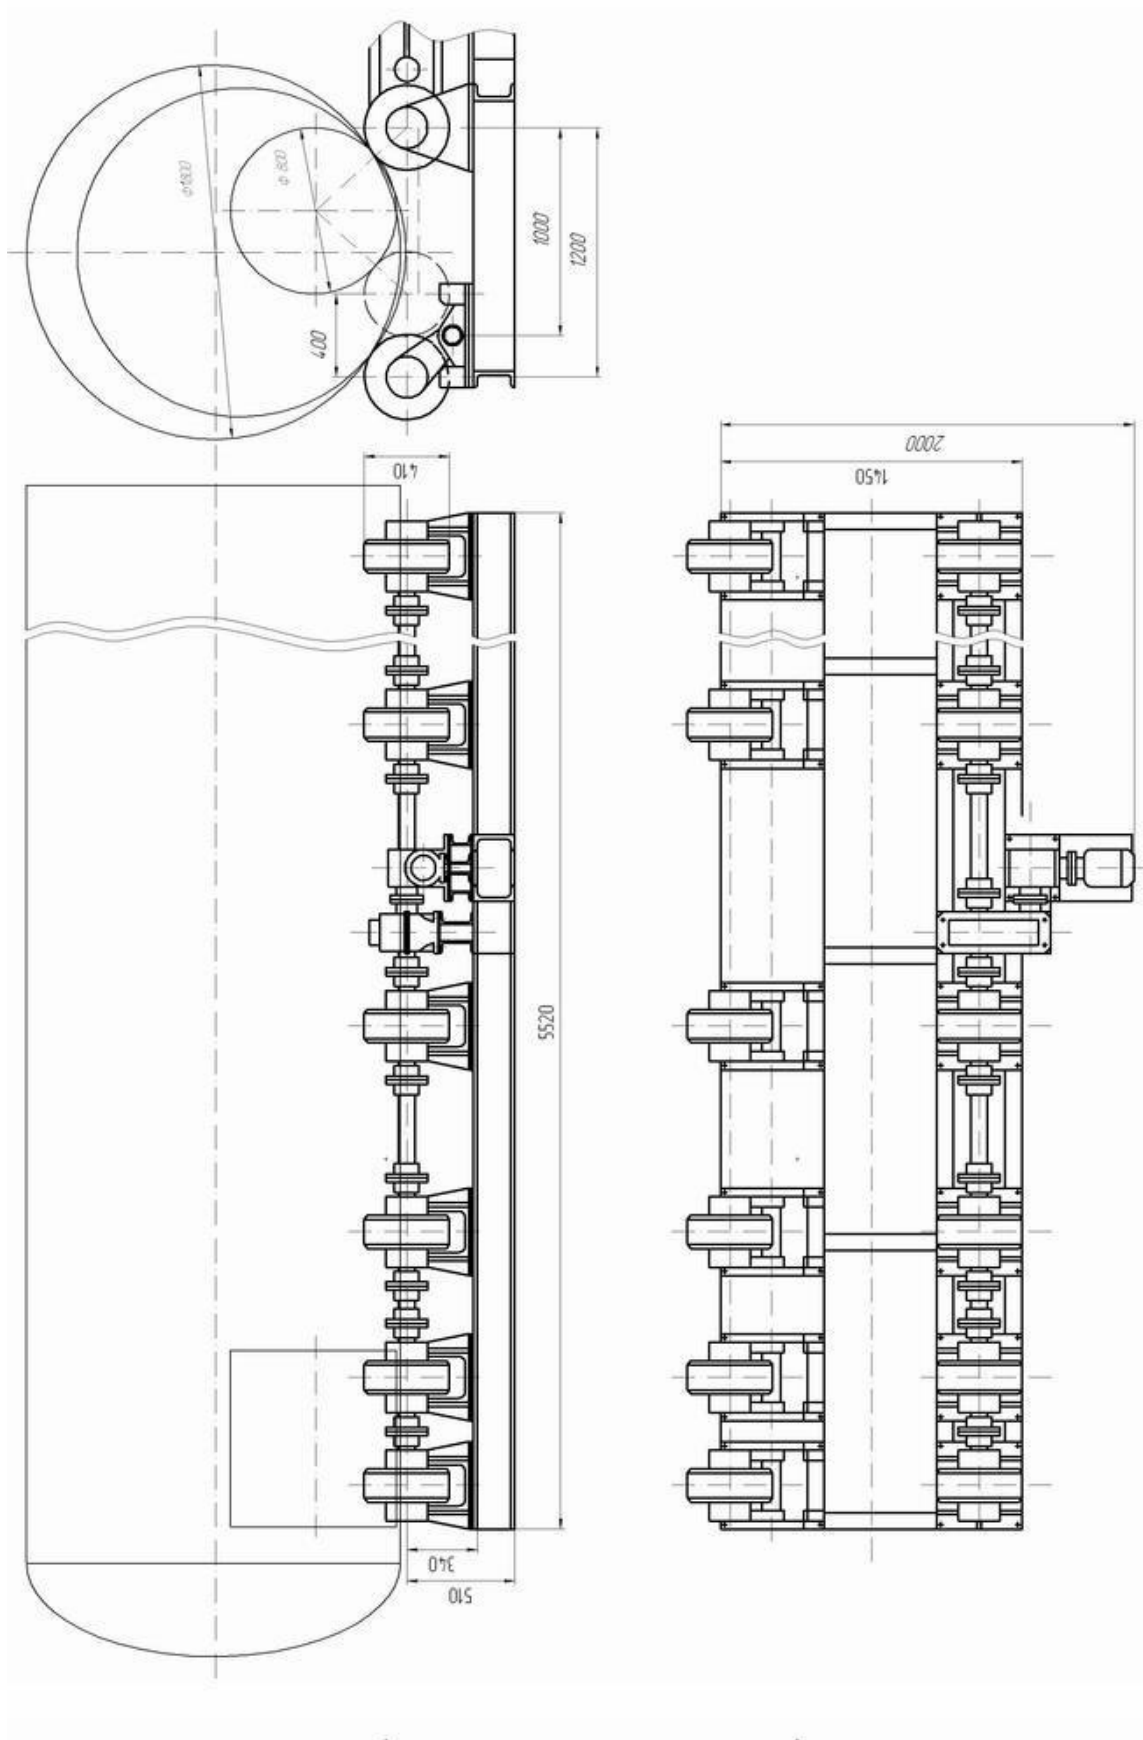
Загальний вигляд роликово-поворотного стенда
